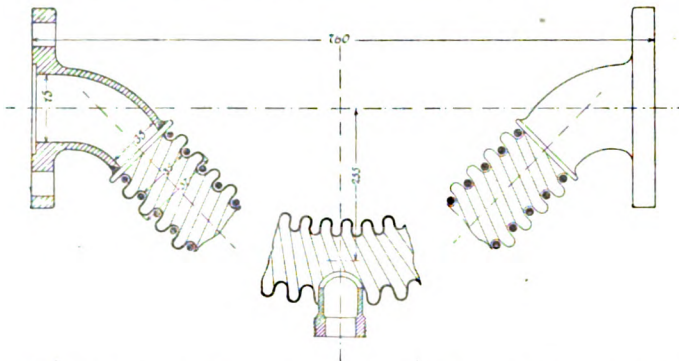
Geschweißter Schlauch als Heizschlauch zwischen Lokomotive und Tender.
